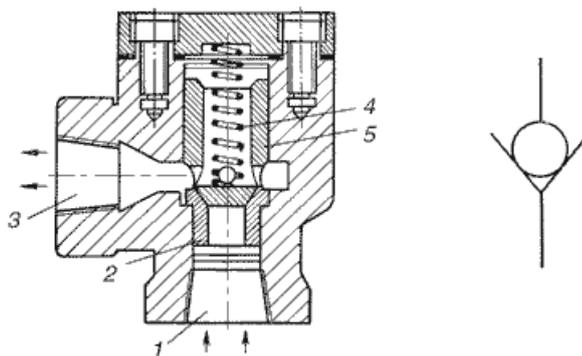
Обратный клапан типа Г51: а - конструкция; б - условное обозначение
